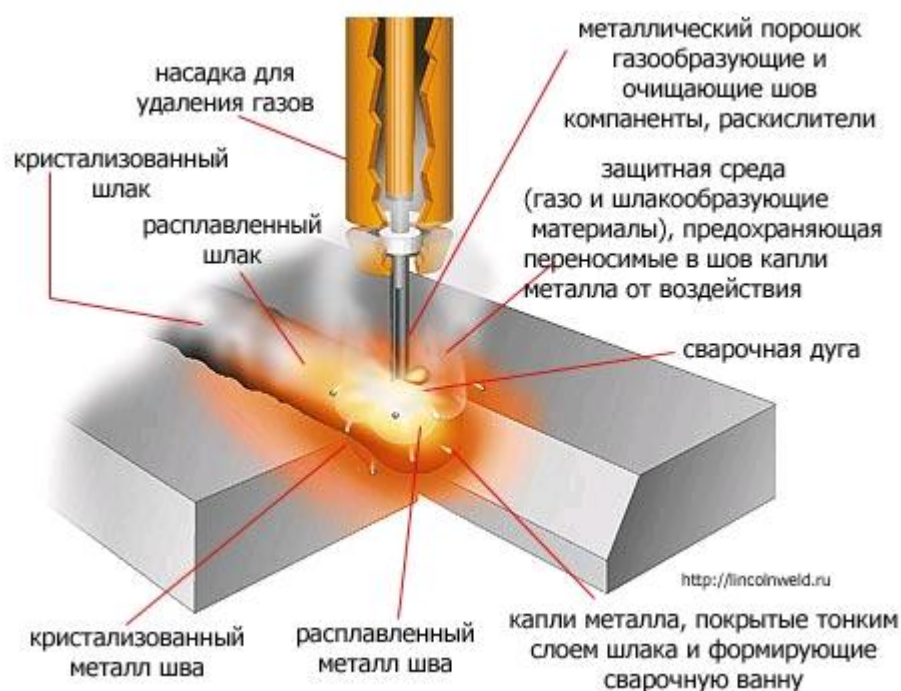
Сварка самозащитной порошковой проволокой
